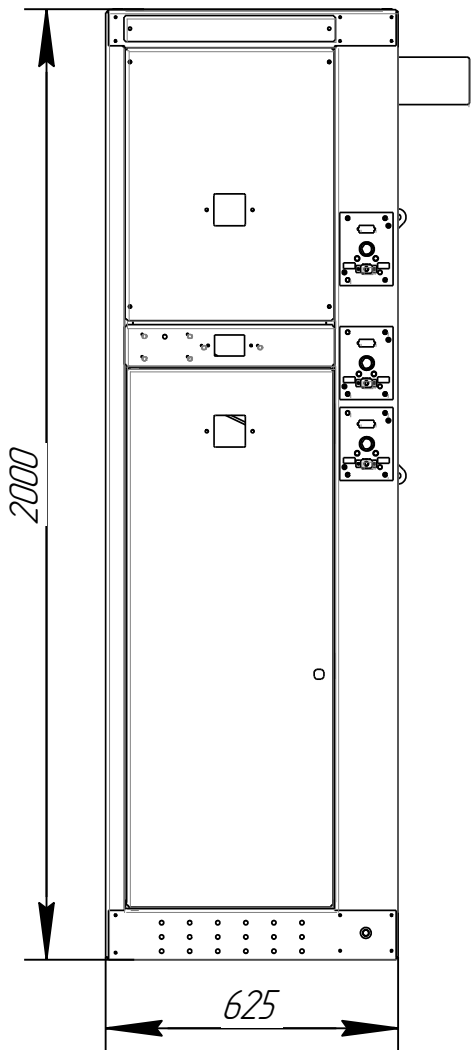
Габаритные размеры камеры КСО - 303 - 05
